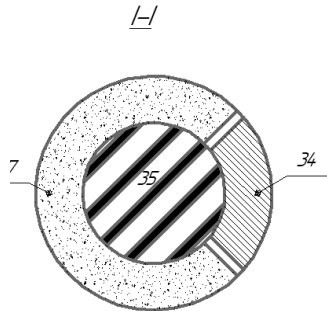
Схема обладнання гирла обсадної колони і з'єднання її башмака з корпусом сорбційної колони
